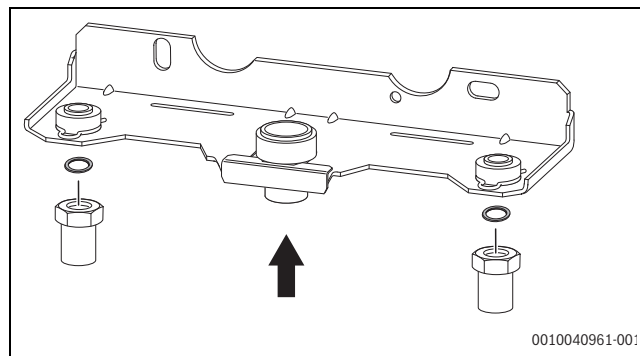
Rohre mit Dichtungen an Montageanschlussplatte montieren
